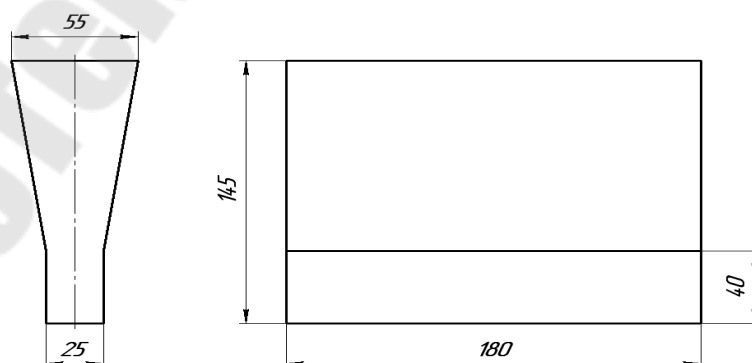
Проба для изготовления образцов для механических испытаний высокопрочного чугуна
